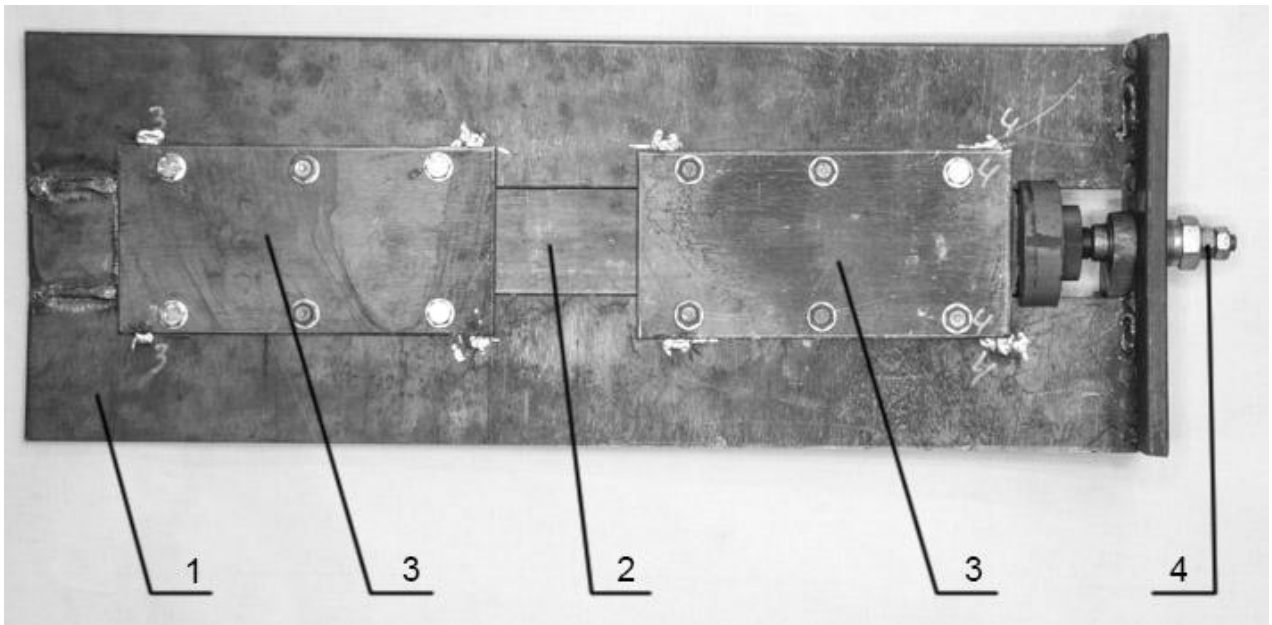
Пристосування для пластичного деформування плоского зразка-балки стисненням в зібраному стані. 1 – корпус пристосування, 2 – зразок-балка, 3 – направляючі накладки (4 шт.), 5 – гвинт для деформування
